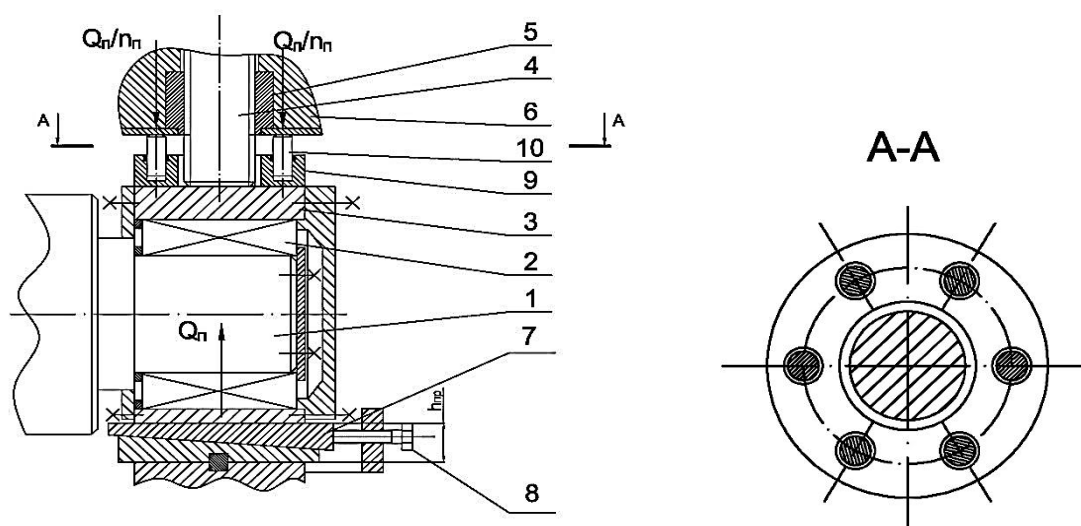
Предлагаемая конструкция комбинированного гидромеханического нажимного механизма чистовых рабочих клеток станов для горячей прокатки полосовых и ленточных заготовок
